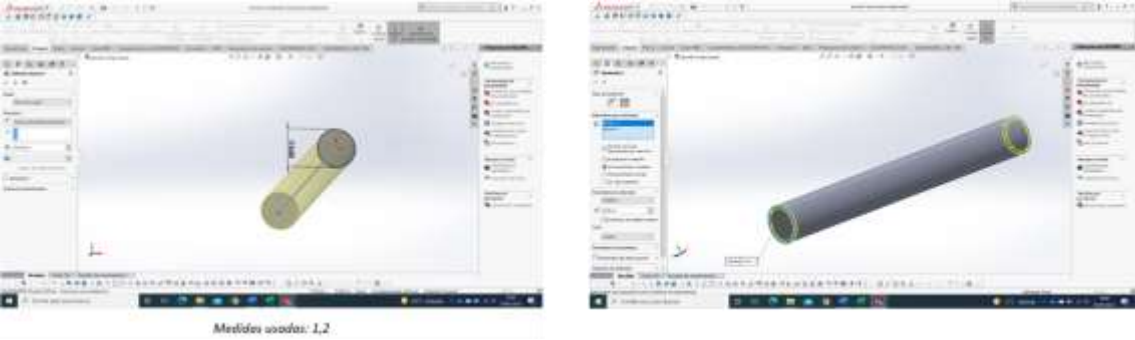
Proceso de diseño del pasador largo de la pieza agujereada
